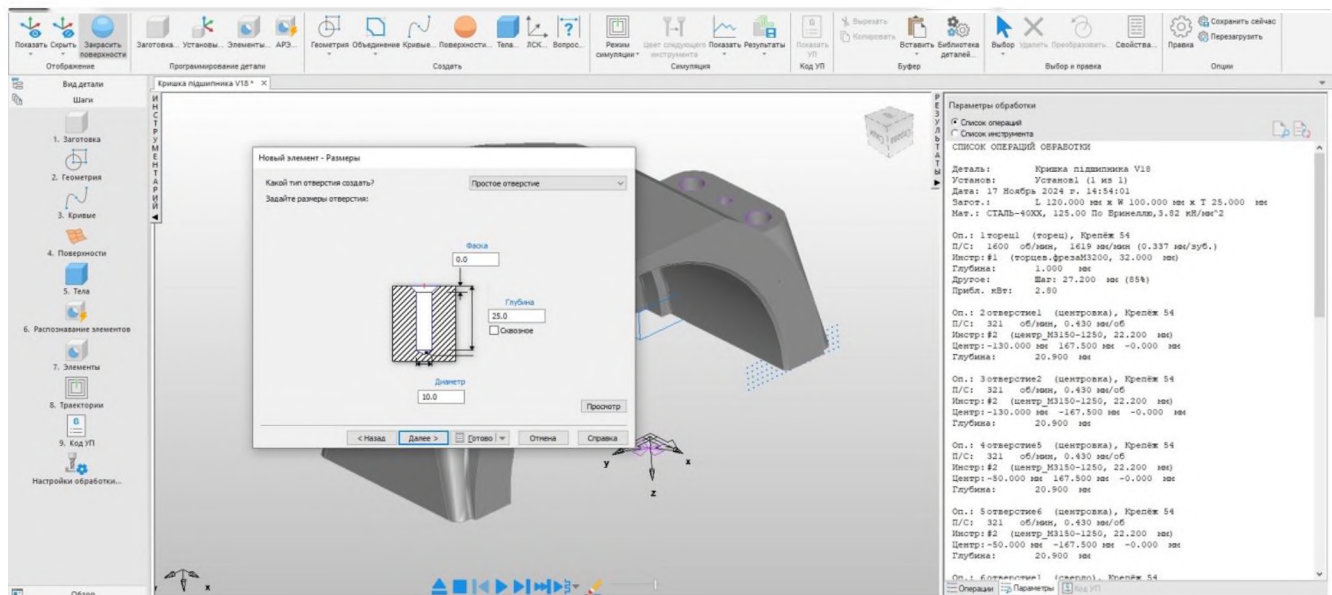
Введення даних для обробки деталі «Корпус підшипника»
